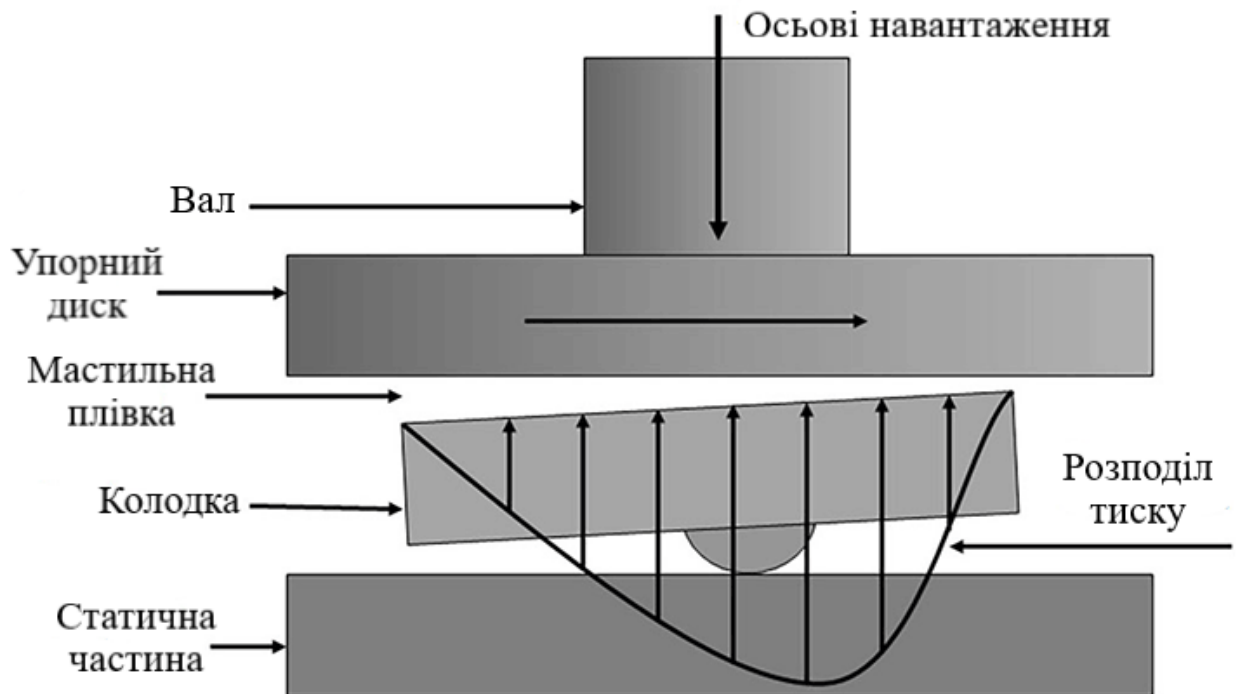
Схема роботи упорного підшипника ковзання[6]
